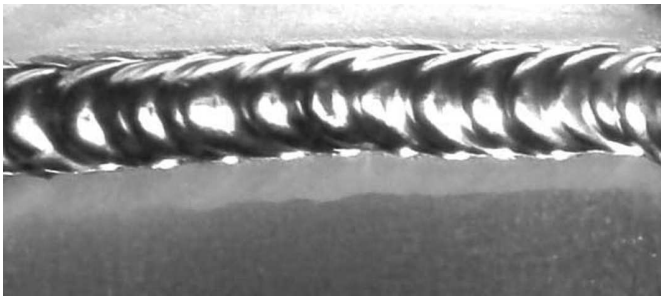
Внешний вид сварного соединения, выполненного ручной сваркой
